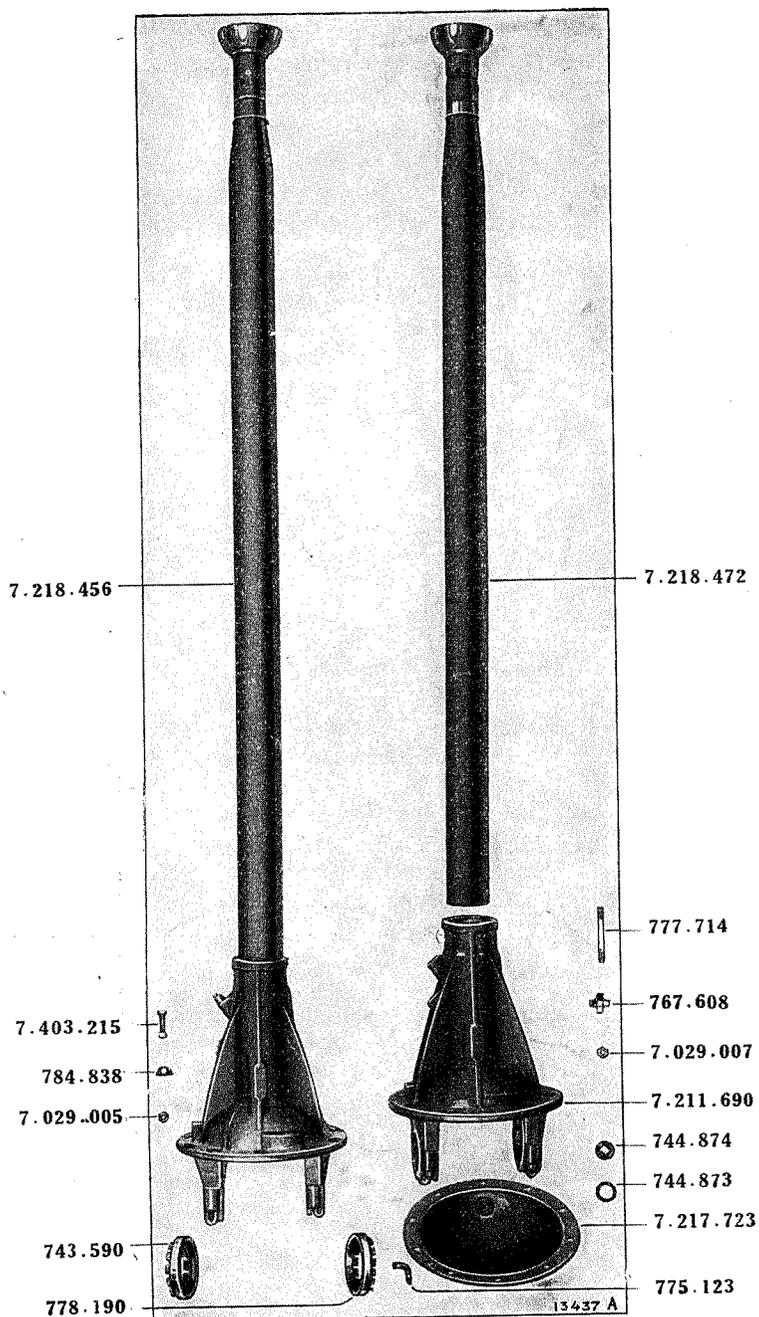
Couvercles, bouchons, tube de poussée et boîtier support de tube conique.
